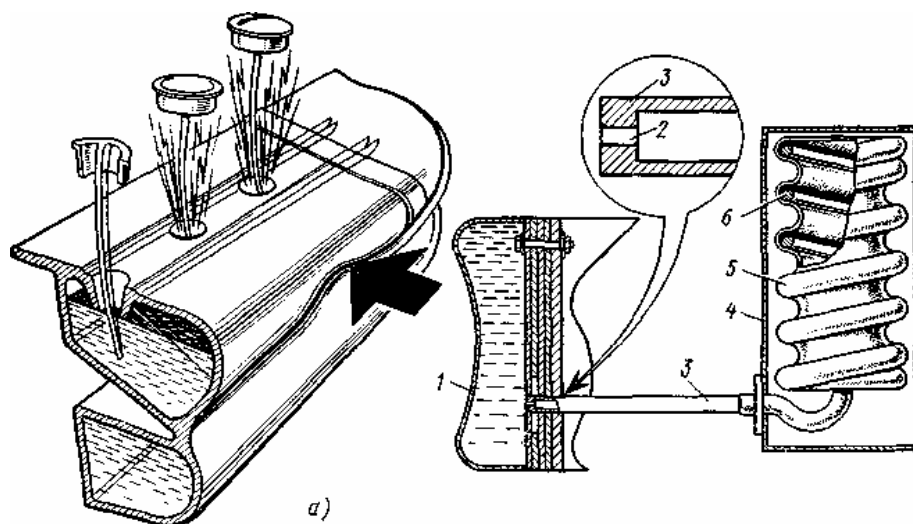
Бампер из синтетических материалов: а — бампер с выбиваемыми заглушками; б — бампер с растягивающимся сильфоном: 1 — упругая оболочка; 2 — суживающаяся часть трубки; 3 — трубка; 4 — корпус; 5 — сильфон; 6 — пружина
